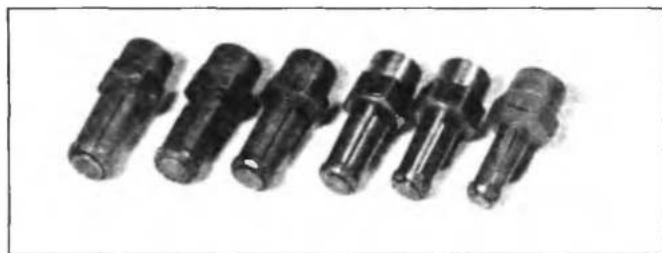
Набор цанг для выпрессовки подшипников из коленчатых валов
